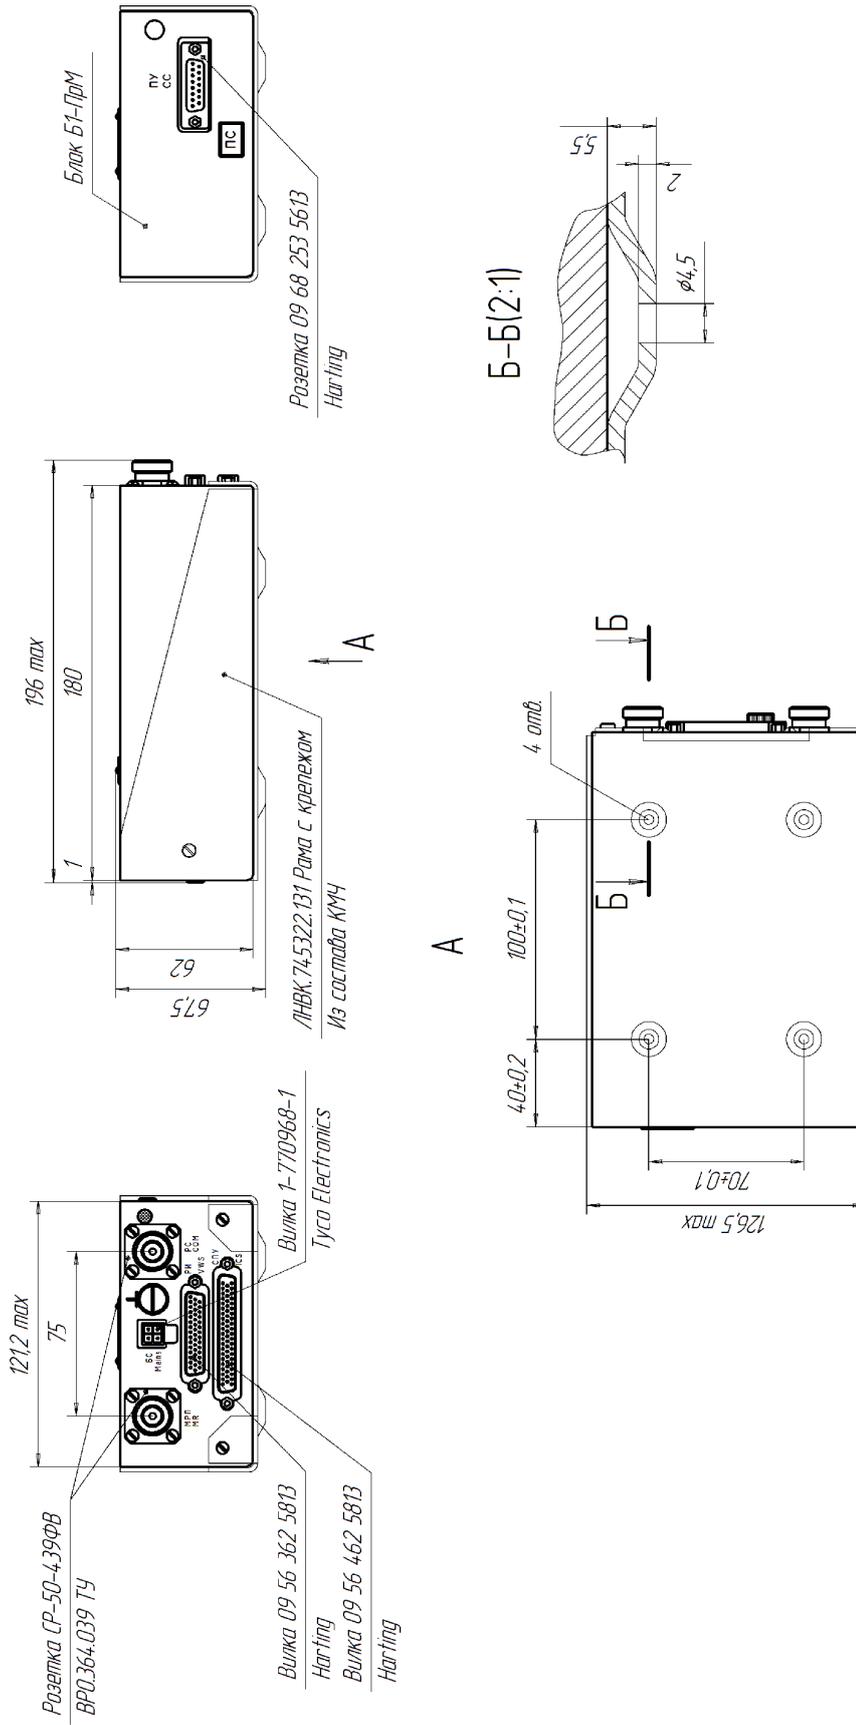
Габаритный чертеж блока Б1-ПрМ на раме
